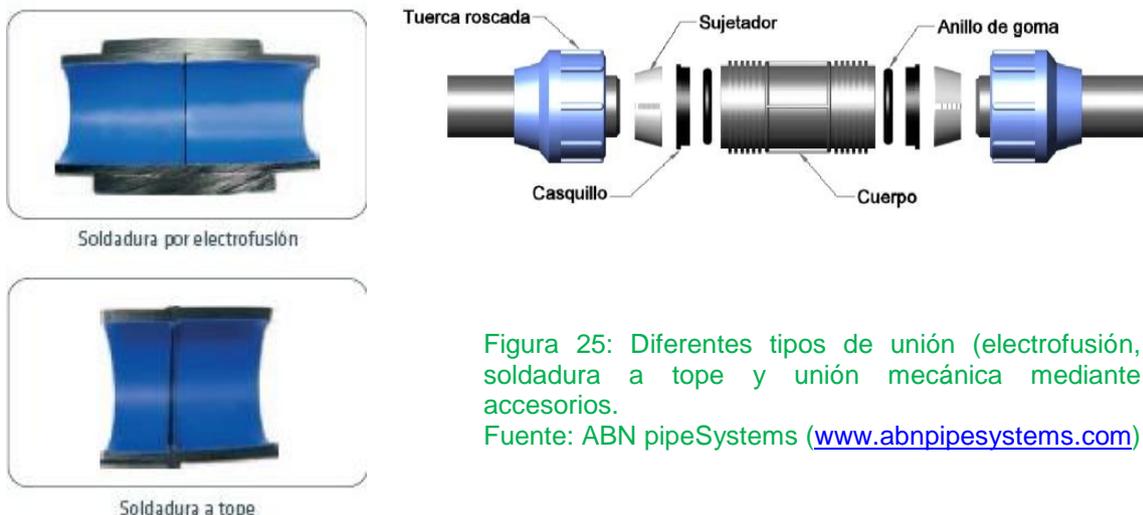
Diferentes tipos de unión (electrofusión, soldadura a tope y unión mecánica mediante accesorios).
